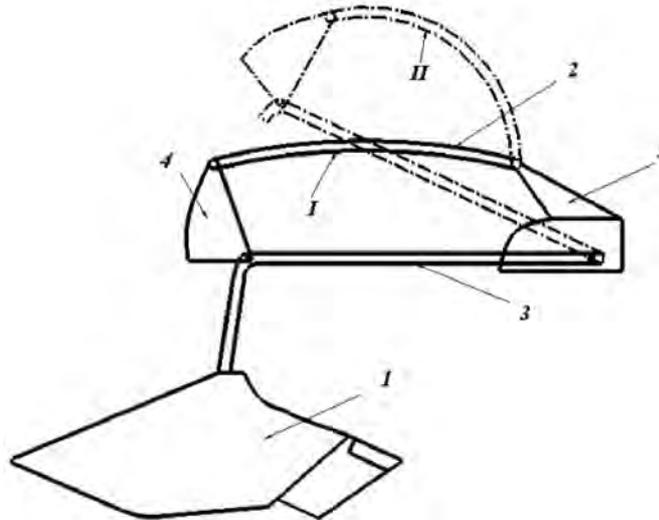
Схема работы защитного механизма корпуса плуга: I – положение рессорной защиты при вспашке; II – положение срабатывания упругого элемента при наезде на препятствие; 1 – Корпус плуга; 2 – Упругий элемент; 3 – Грядиль; 4 – Кронштейн подвижный; 5 – Кронштейн неподвижный
